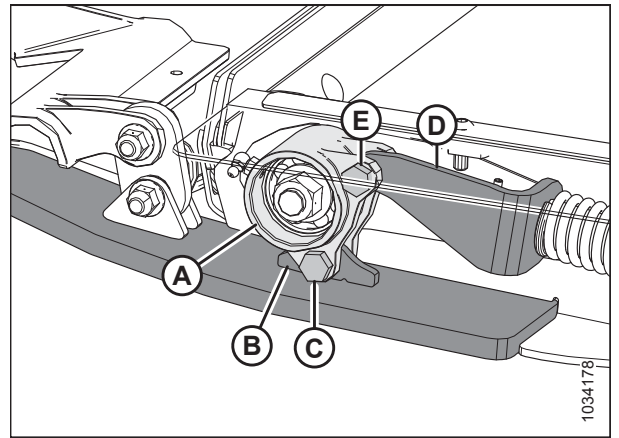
Rodamiento de rodillo tensor: lado izquierdo
